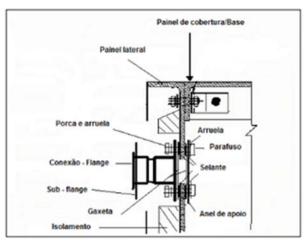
Conexão de flange - detalhes de fixação e selagem, conforme o manual técnico do fabricante
